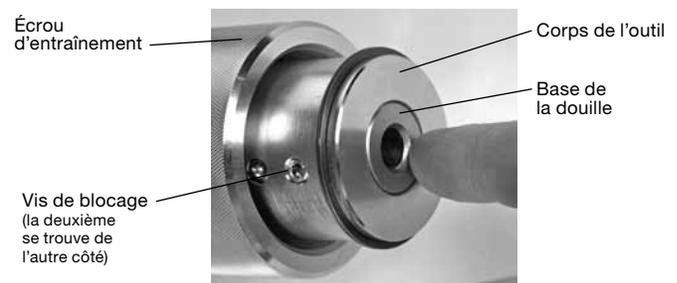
Montage de la douille de l'outil à usiner des cônes
